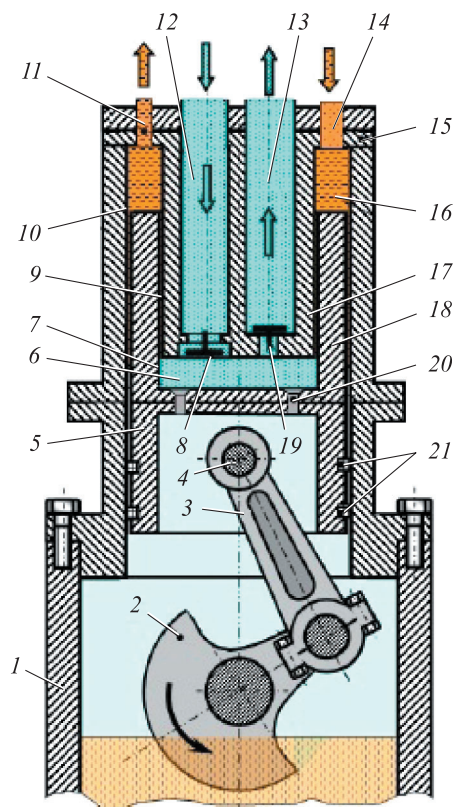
Схема продольного сечения экспериментального образца ПГЭМОД: 1 — картер; 2 — коленчатый вал; 3 — шатун; 4 — поршневой палец; 5 и 18 — поршень и его кольцевой П-образный выступ; 6 и 16 — компрессорная и насосная полости; 7 и 10 — газовый и жидкостный цилиндры; 8 — всасывающий клапан компрессора; 9 — рабочий зазор; 11, 13 — полости нагнетания; 12, 14 — полости всасывания; 15 и 17 — клапанная крышка КС и ее выступ; 19 — нагнетательный клапан компрессора; 20 — винт; 21 — уплотнительные кольца
